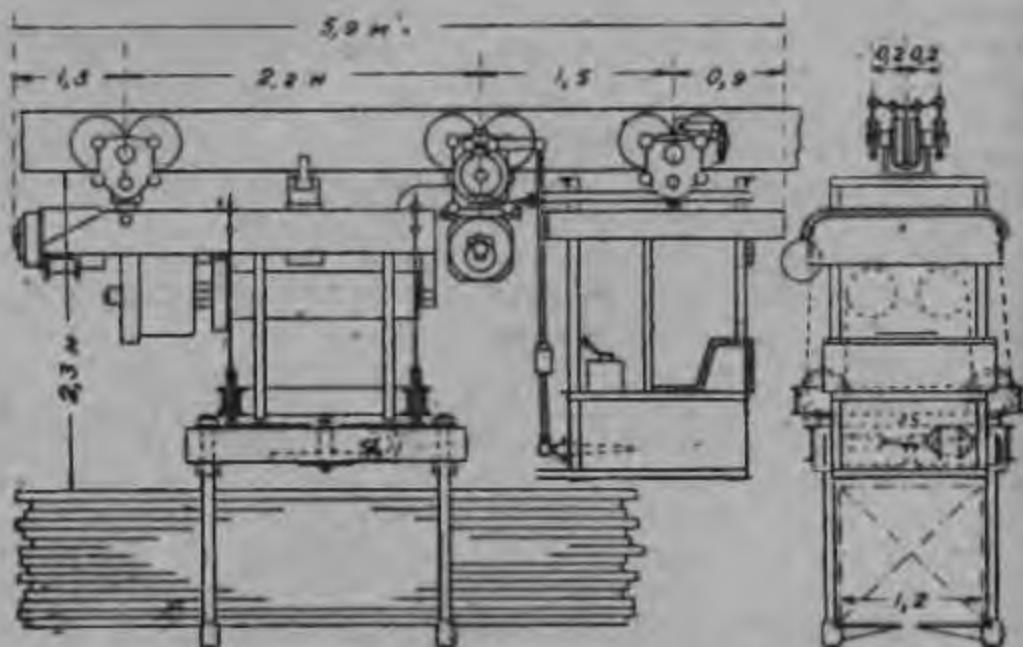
Захватная рама специальной конструкции для перегрузки пиломатериалов.
